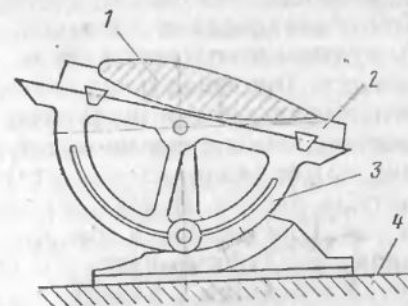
Угломер с шаблоном для проверки угла установки сечения лопасти
